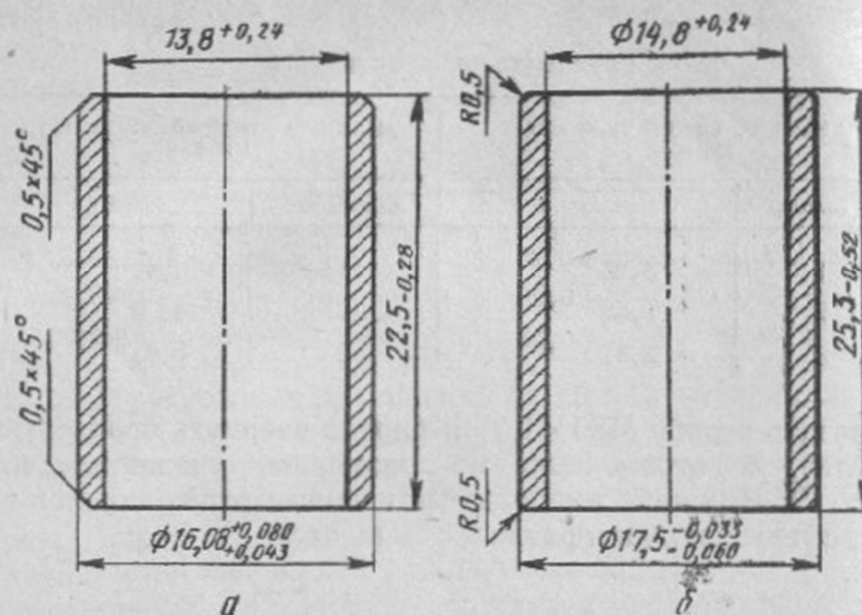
Чертеж втулки ремонтной верхней головки шатуна:
